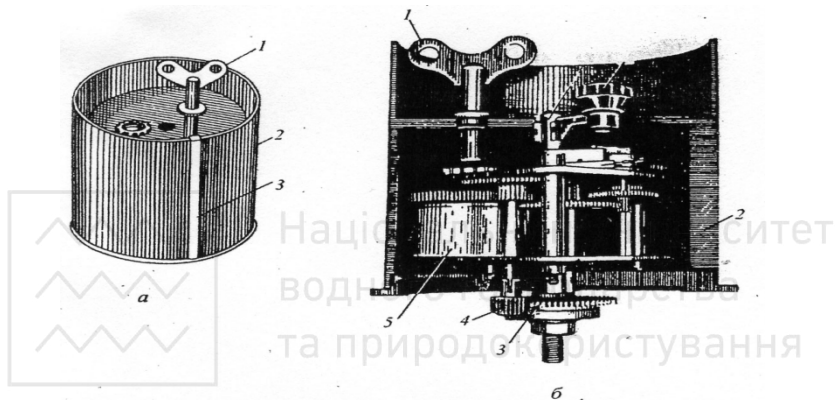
Барабан з годинниковим механізмом: а – загальний вигляд; 1 – заводний ключ; 2 – корпус барабана; 3- жазивна пружина; б – розріз: 3 – нерухома шестерня; 4 – шестерня, яка обертається годинниковим механізмом (трибка); 5- барабан з пружиною [4]
